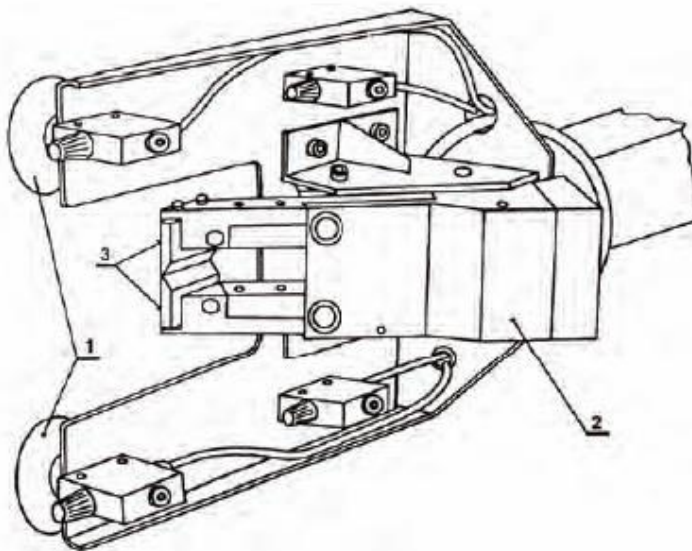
Možné principy řešení MÚH typu T4 [14]
